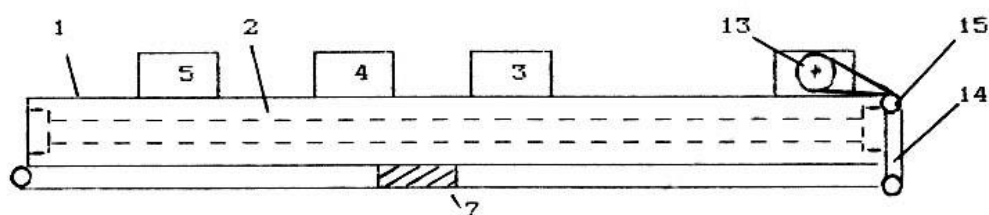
Общий вид светоловушки по а.с. 1685346: 1 - корпус; 2 – разрядная лампа; 3 - ПРА; 4 - высоковольтный трансформатор; 5 - ЛН; 7 - планка; 13 - шкив; 14 - трос; 15 - блоки
